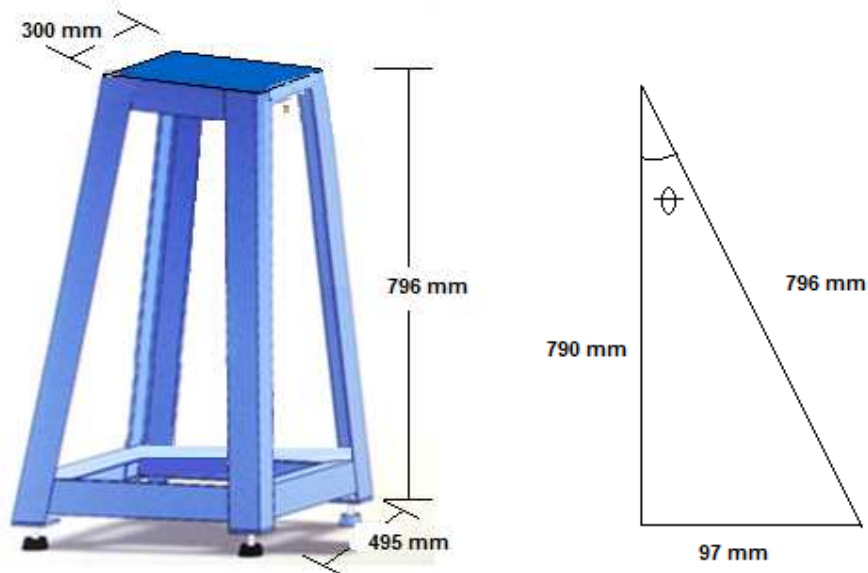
diseño estructura Arreglo utilizado para hacer el cálculo.
